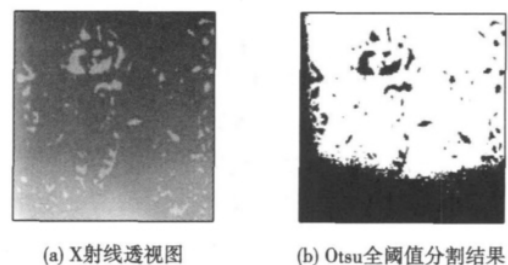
功率三极管 DIE 焊接气泡的全阈值检测
